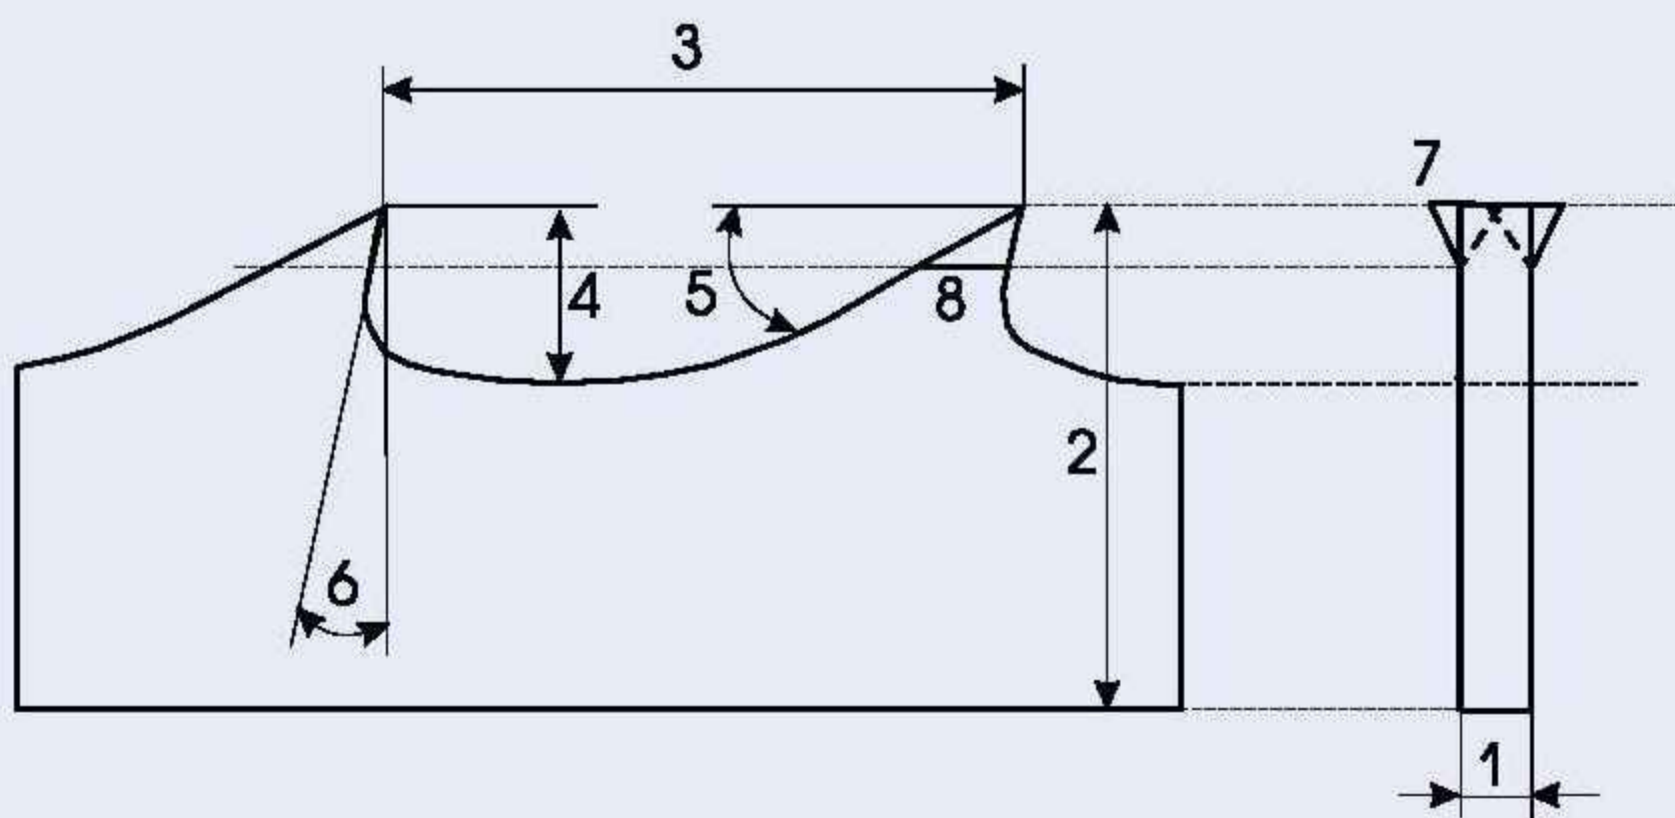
Основные параметры ленточной пилы: 1) толщина; 2) ширина; 3) шаг зубьев пилы; 4) глубина впадины – высота зуба; 5) задний угол; 6) передний угол; 7) развод; 8) линия развода зуба
